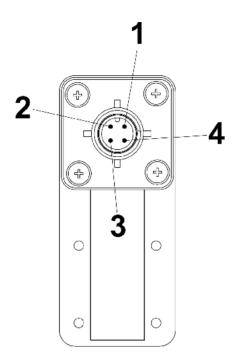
Pin-Belegung Gerätestecker M12x1 (Form 30x70)
